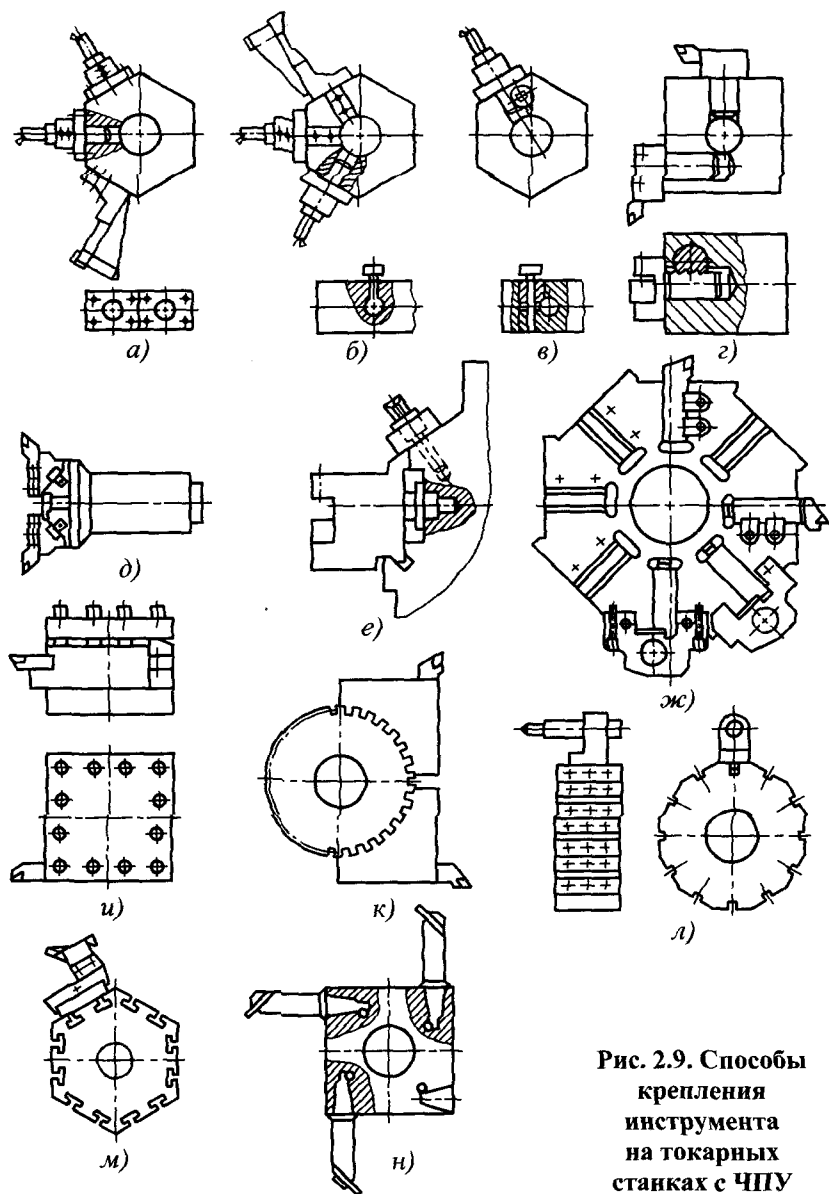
Способы крепления инструмента на токарных станках с ЧПУ
